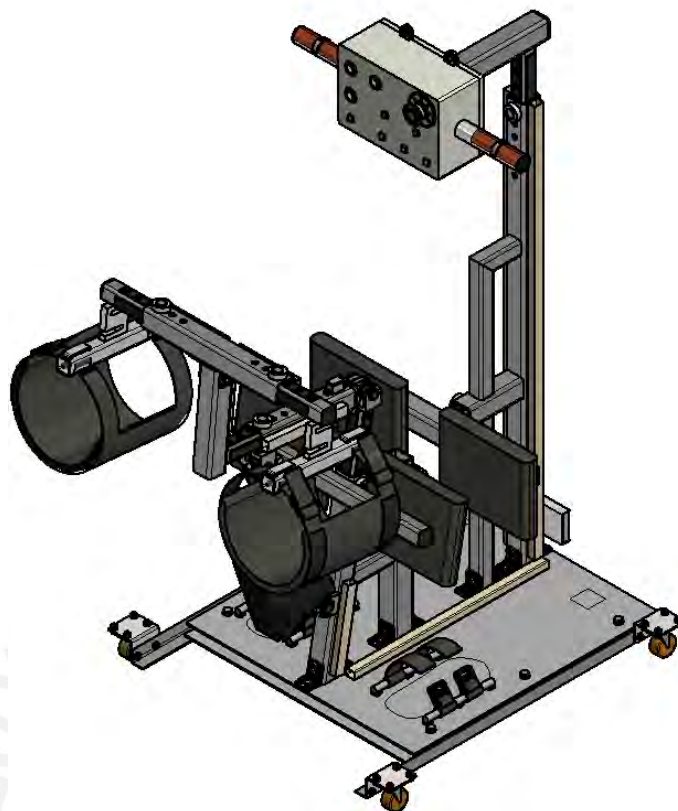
Vista en isométrico del diseño final del dispositivo.
